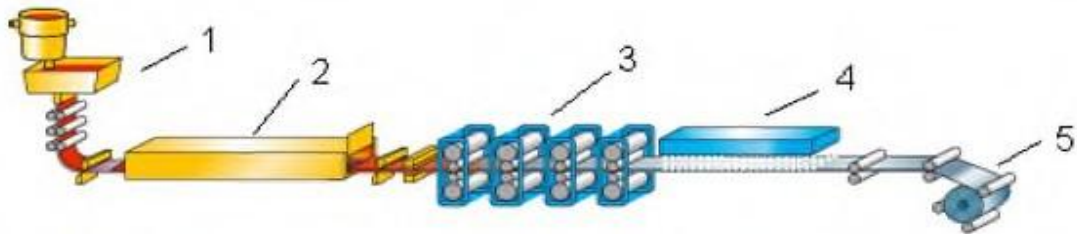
Агрегат CSP прямої прокатки смуги: 1 – машина безперервної розливки; 2 – піч; 3 – прокатні кліті; 4 – ділянка охолодження; 5 – моталки
